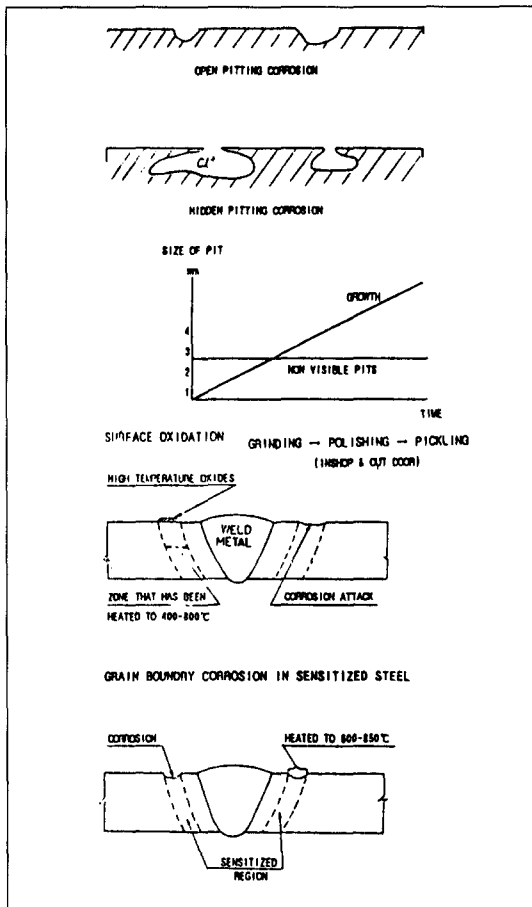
일반적인 Corrosion 형태와 용접 부식 현상
